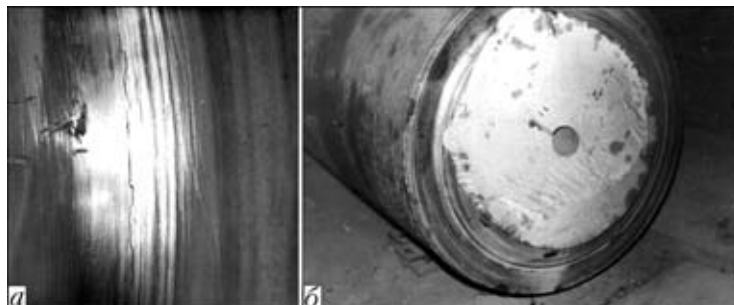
Внешний вид галтельной части прокатного валка с трещиной на поверхности (а) и зоны разрушения горизонтального валка стана слябинг-1150 по галтели (б)
